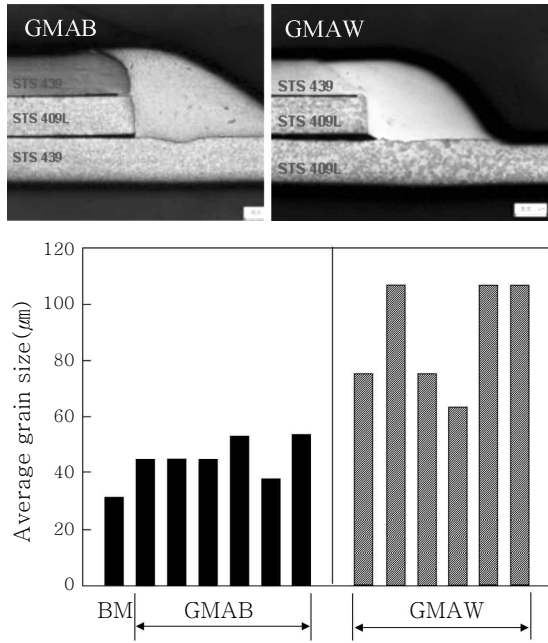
GMAW 및 GMAB 용접부 조직 및 용접 열영향부 결정립 크기
